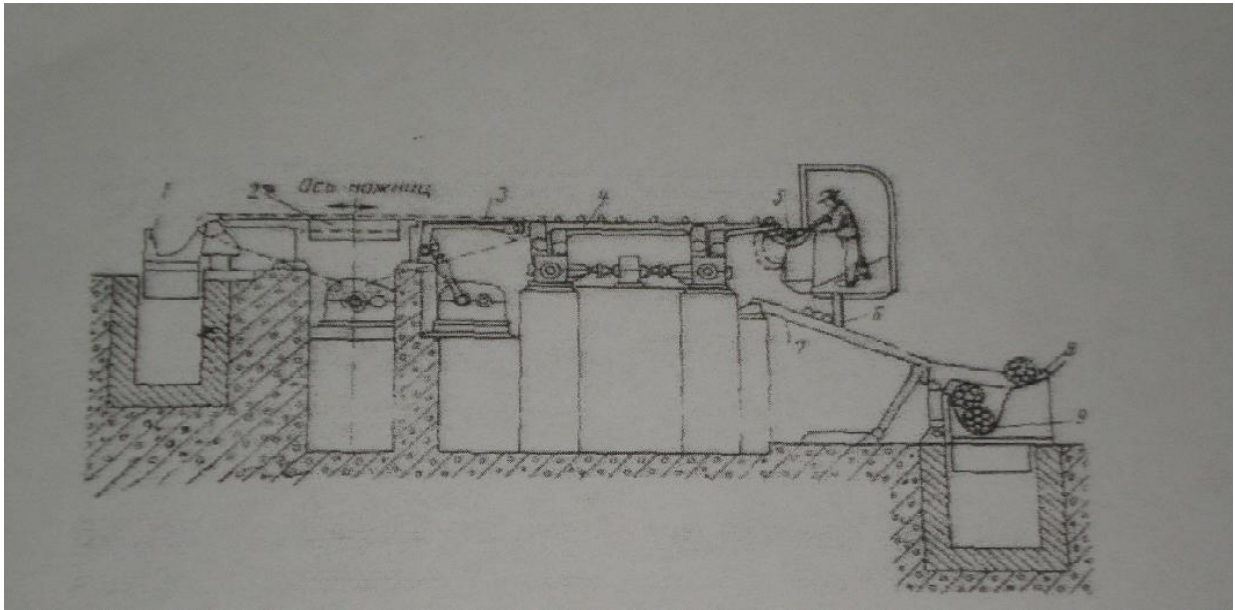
Пакетуєча установка і ручна обв'язка сортового прокату
